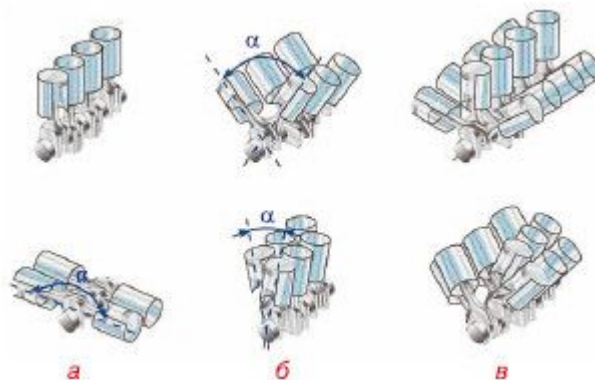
Схемы расположения цилиндров в двигателях различной компоновки:
